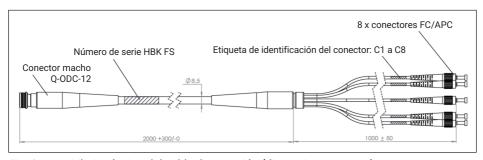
Dibujo técnico del cable de conexión (dimensiones en mm)
